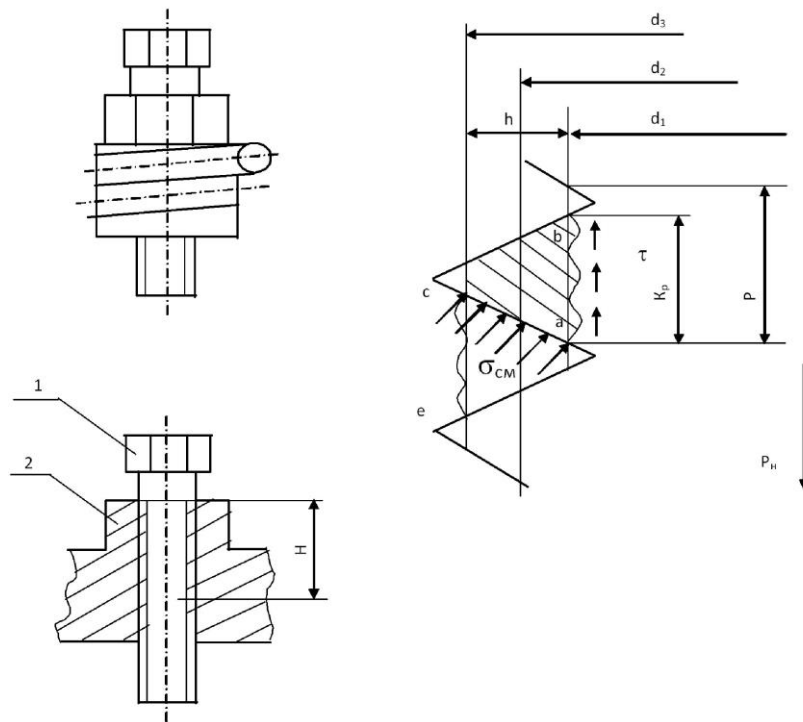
Схема болтового з'єднання: 1-болт (Сталь 35); 2- корпусна деталь з різьбою (Відливка КЧ 33-8-Ф).
